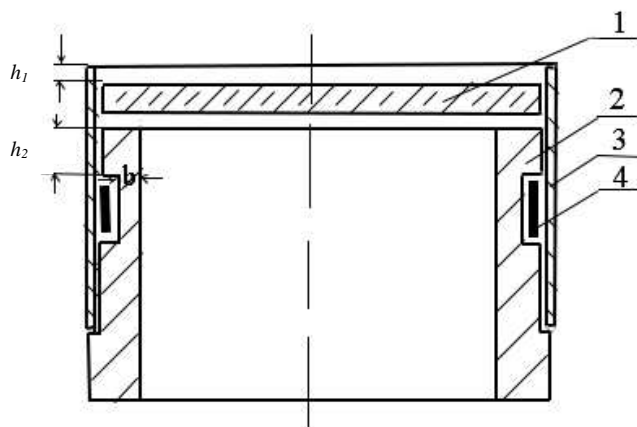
Конструкция паяного соединения тонкого неметаллического диска с полым тонкостенным металлическим цилиндром: 1 — диск; 2 — цилиндр; 3 — фольга; 4 — припой; h_1 — высота компенсирующего конца; h_2 — высота опорного конца рабочей детали; b — толщина корпуса в зоне припоя
